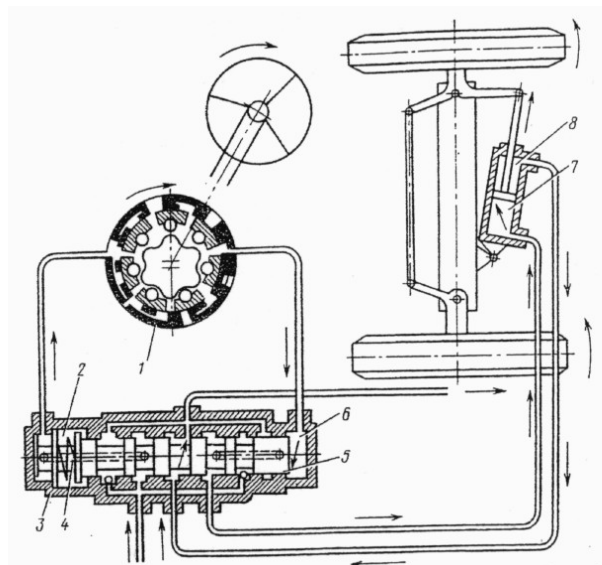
Схема гидравлического управления самоходными машинами: 1 - насос-дозатор; 2, 6 - полости распределителя; 3 - крышка; 4 - пружина; 5 - золотник; 7, 8 - полости гидроцилиндра
